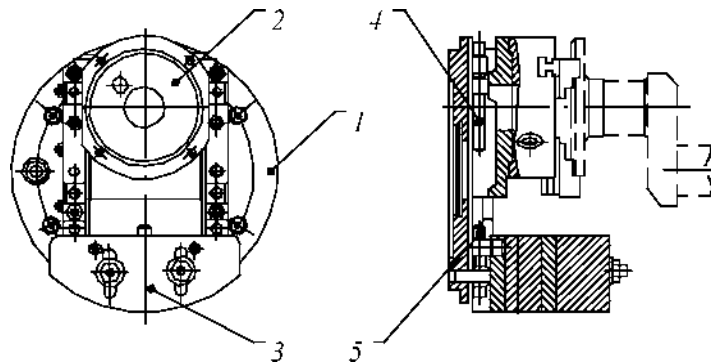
Центрозмішувач до верстата моделі 3А423: 1 - корпус; 2 - трикулачковий патрон; 3 - вантажі балансування; 4, 5 - регулювальні гвинти
